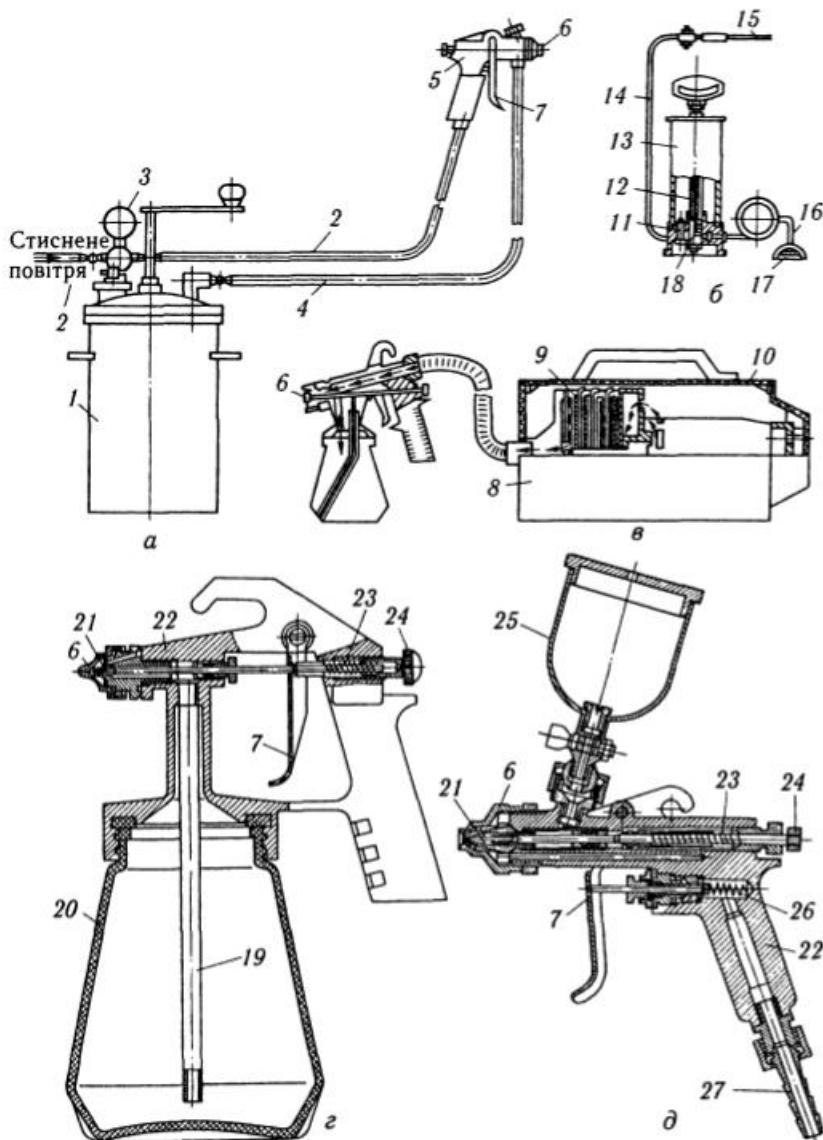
Пневматичні установки для фарбування поверхонь:
